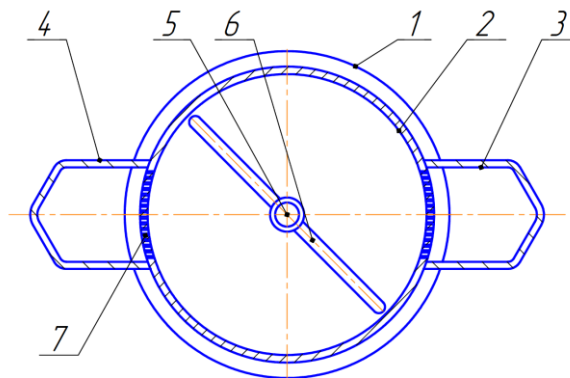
Дробарка кормів: 1 – корпус; 2 - дека; 3, 4 – вивантажувальний патрубок; 5 – вал; 6 – робочий орган; 7 – решітна вставка.
